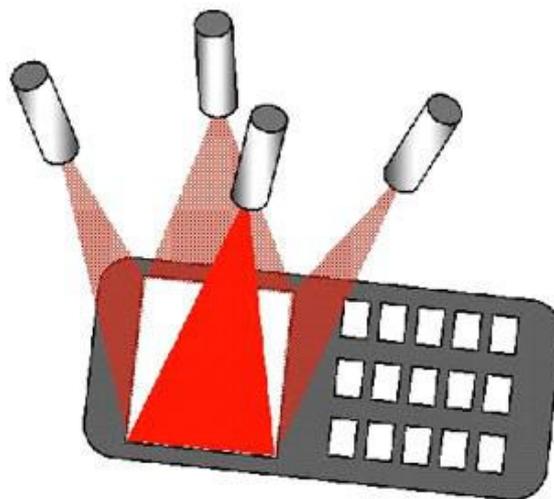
Simultanschweißen (simultaneous welding)
